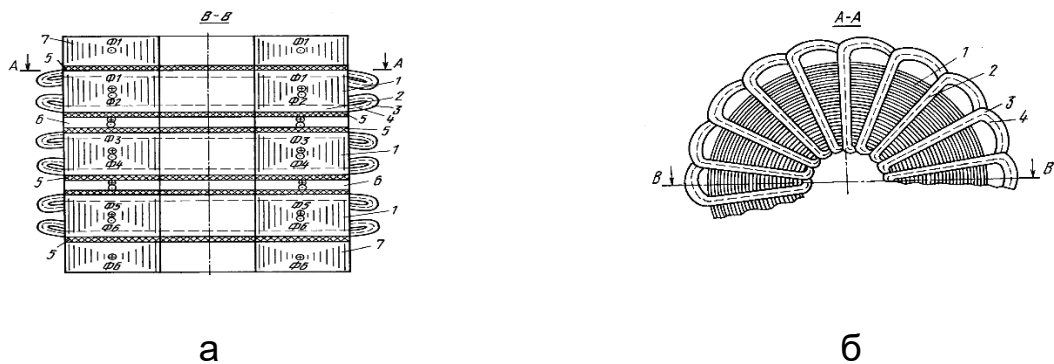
Агрегатированный трансформатор: а - вид спереди; б - вид сверху
